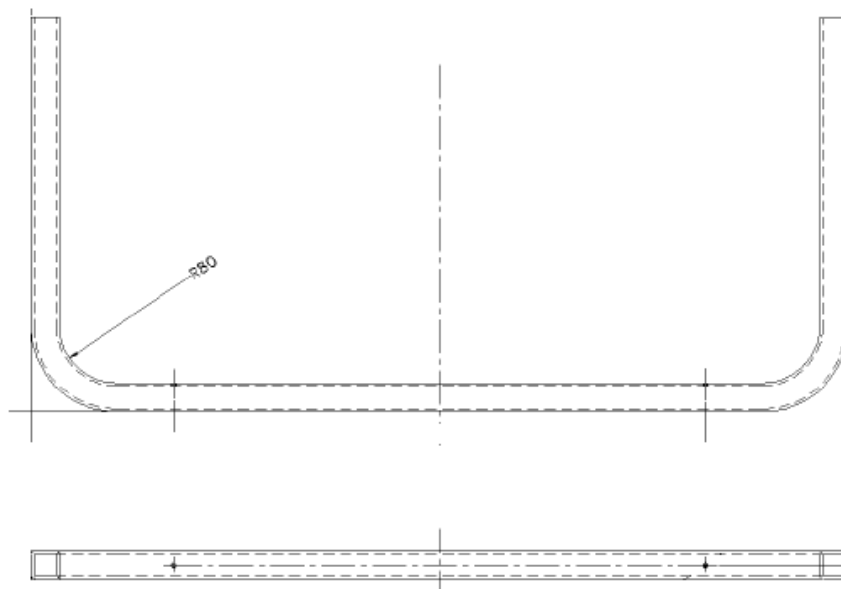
disegno tecnico del tubo di sollevamento
